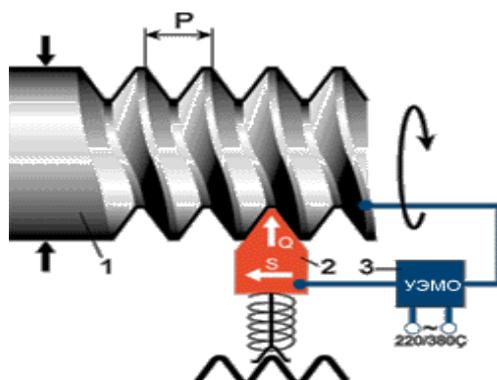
Схема ОУЭМО (1 – заготовка, 2 – инструмент, 3 – оборудование ОУЭМО)
